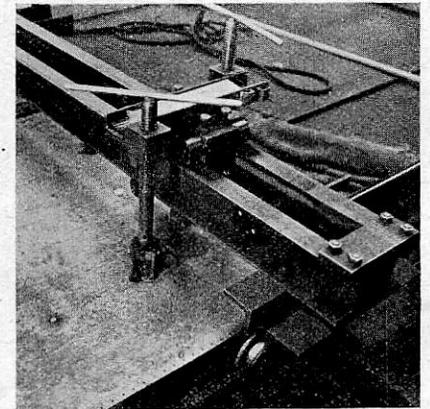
Bewegliche Spannvorrichtung für das Aufschweißen des Seitenwandbleches auf das Gerippe mit Lochschweißung.
